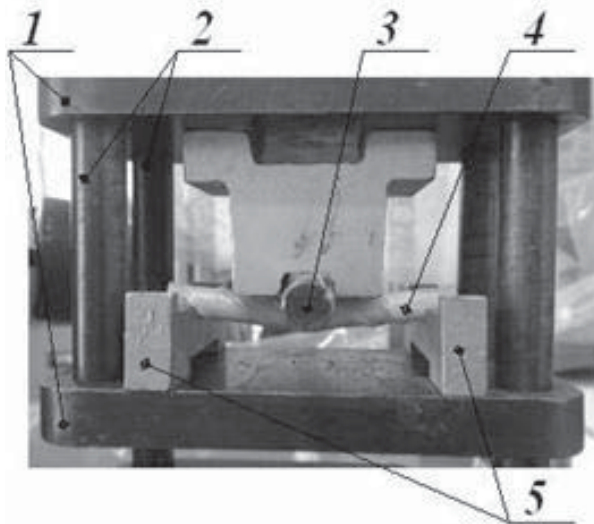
Нагрузочное устройство: 1 – опорные плиты; 2 – направляющие; 3 – цилиндрический демпфер; 4 – исследуемый образец; 5 – центрирующие опоры
